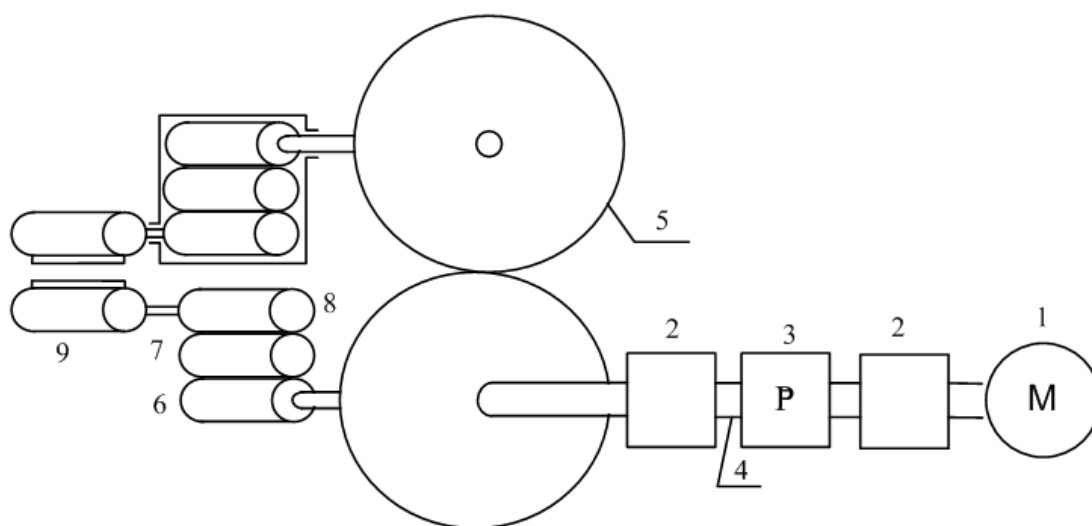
Кинематическая схема барабанных ножниц с поступательно движущимися ножами. 1 - двигатель; 2 - муфта; 3 - редуктор; 4 - вал; 5 - большая шестерня; 6 -солнечная шестерня, 7 - промежуточная шестерня; 8 - планетарная шестерня; 9 - ножи
